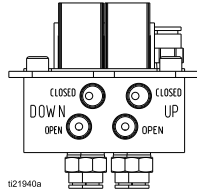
Schlauchanschlüsse am Magnetventilverteiler, zum Pumpenauslassverteiler
